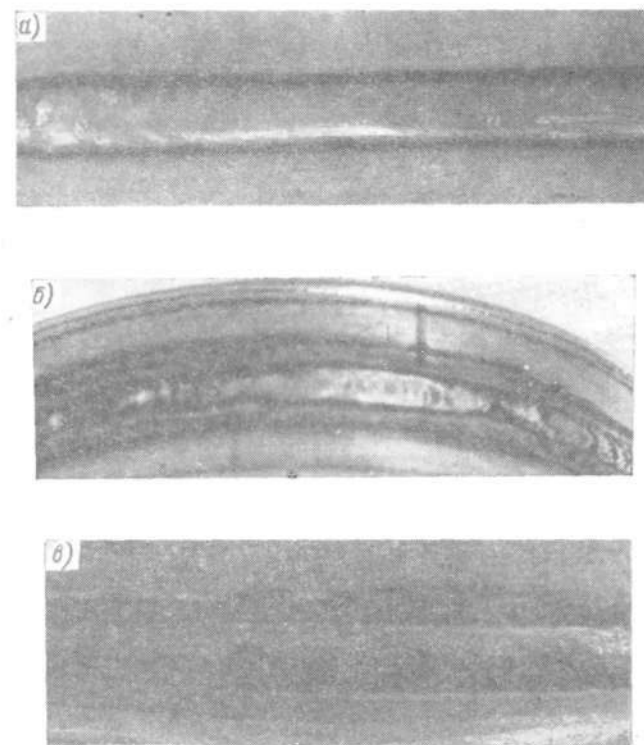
Внешний вид швов с различной защитой от воздуха: а — хорошая защита при сварке в стык бескосого соединения; б — удовлетворительная защита при сварке стыкового соединения труб с присадкой; в — плохая защита при сварке листов.
